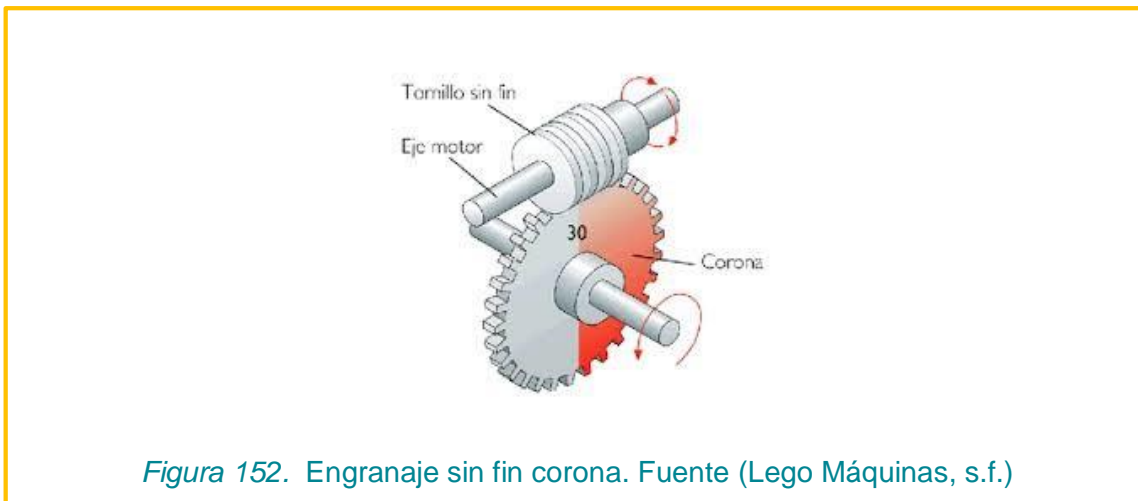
Engranaje sin fin corona. Fuente (Lego Máquinas, s.f.)
